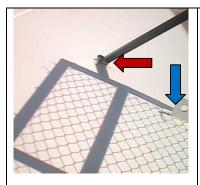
Superficie mal soldada del tanque de Fuel Oil.
